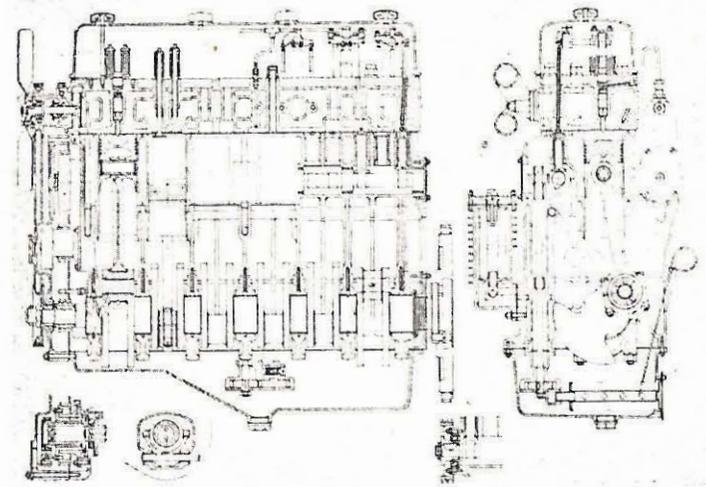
Schnelllaufender 6-Zylinder-Saurer-Dieselmotor P.D.
